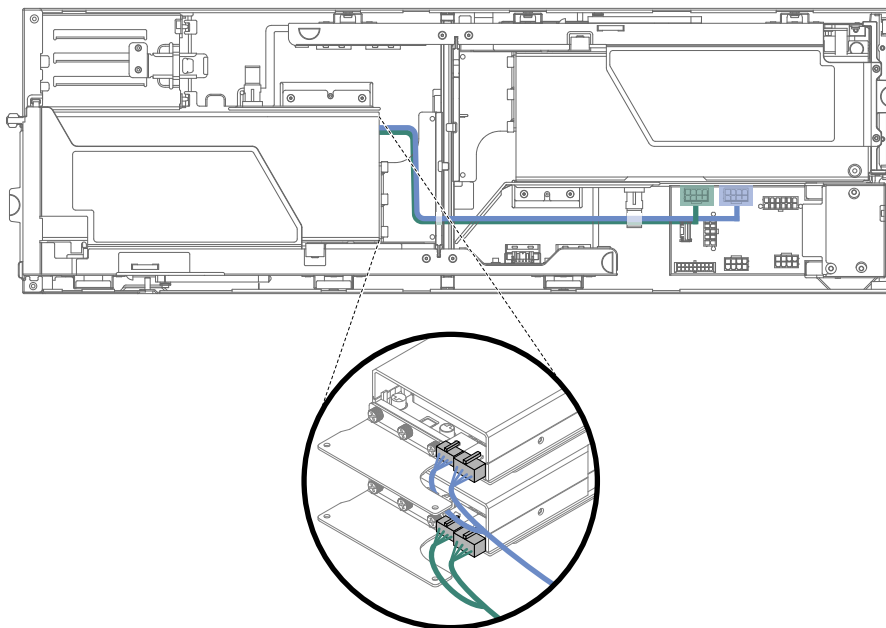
Adaptadores GPU do conjunto do PCI frontal/traseiro com conexão do cabo de alimentação da placa GPU
